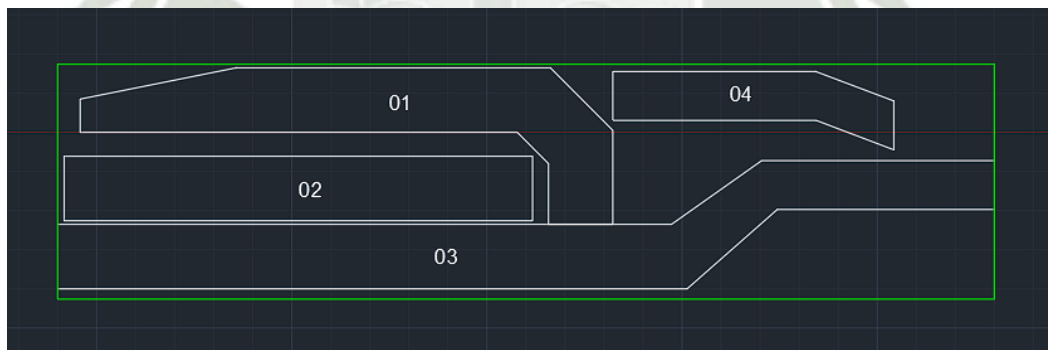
Cortes de Planchas para armado de Viga Principal
